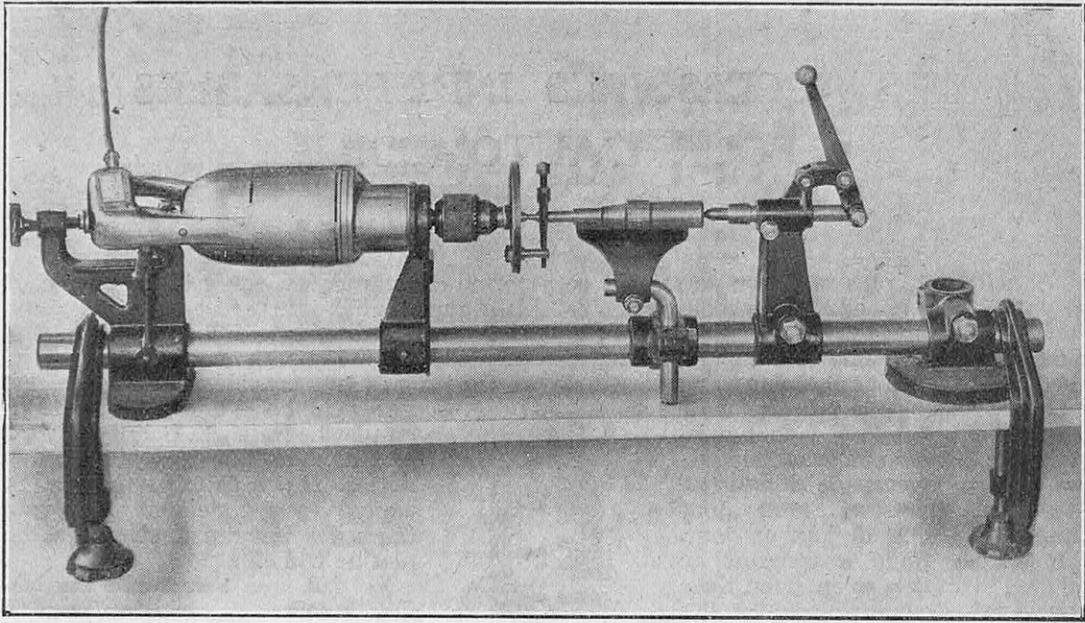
QUELQUES APPLICATIONS DE LA MACHINE HORIZONTALE
